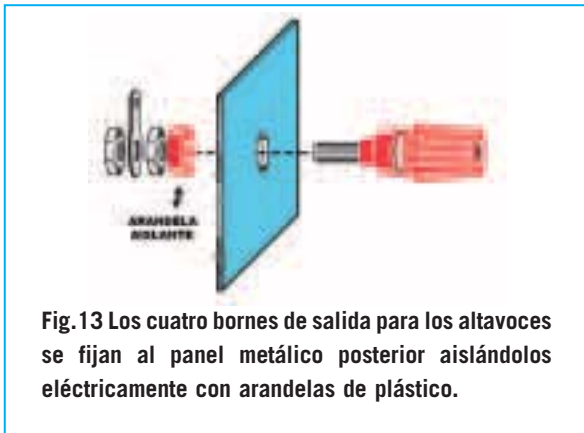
Los cuatro bornes de salida para los altavoces se fijan al panel metálico posterior aislándolos eléctricamente con arandelas de plástico.
